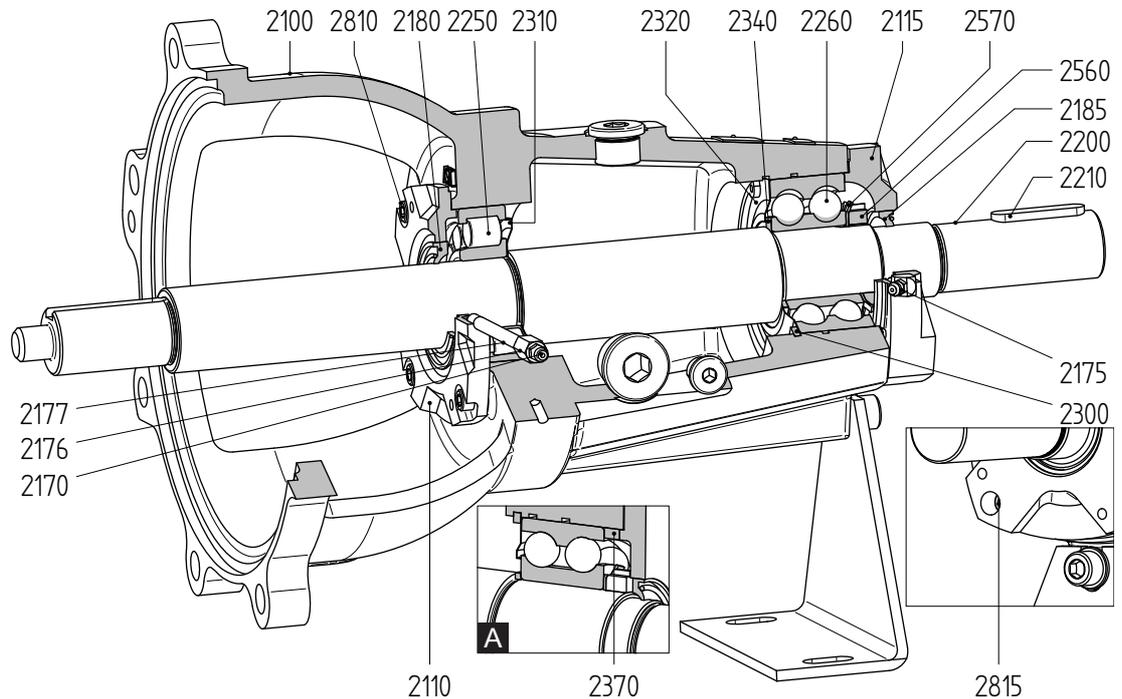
Подшипник L2 (усиленный, с консистентной смазкой) (A = группа подшипников 3)
